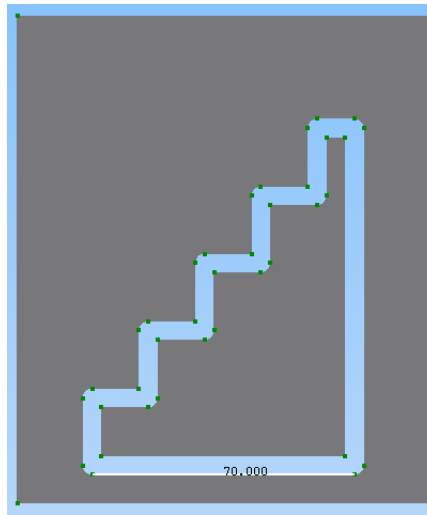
Контроль розміру оброблюваної деталі
